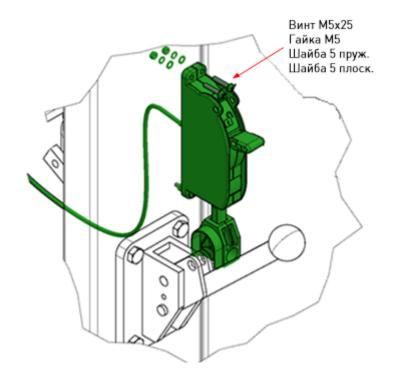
Установка блокиратора с разнесенными разъеденителями
